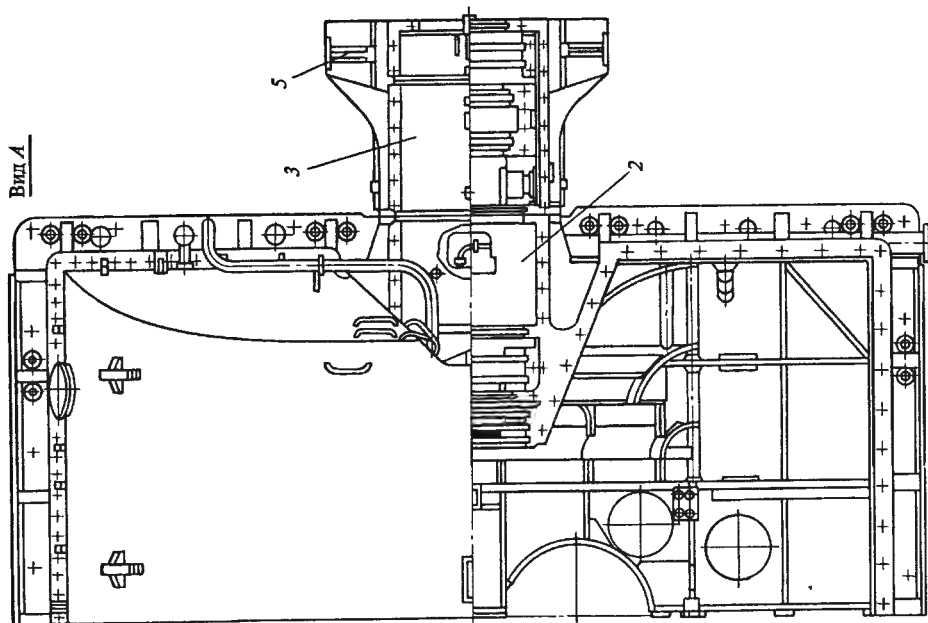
Корпус ЦНД турбины К-500-5/50 с приставной опорой упорного подшипника:
